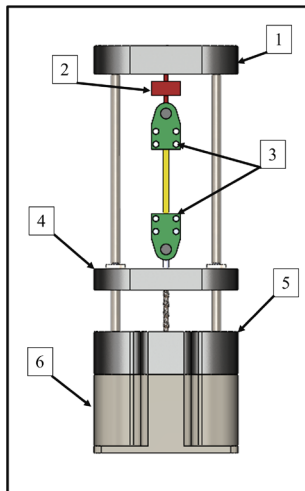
Конструкція другого прототипу: 1 – нерухома траверса; 2 – силовимірвач; 3 – захвати; 4 – рухома траверса; 5 – станина; 6 – опора
